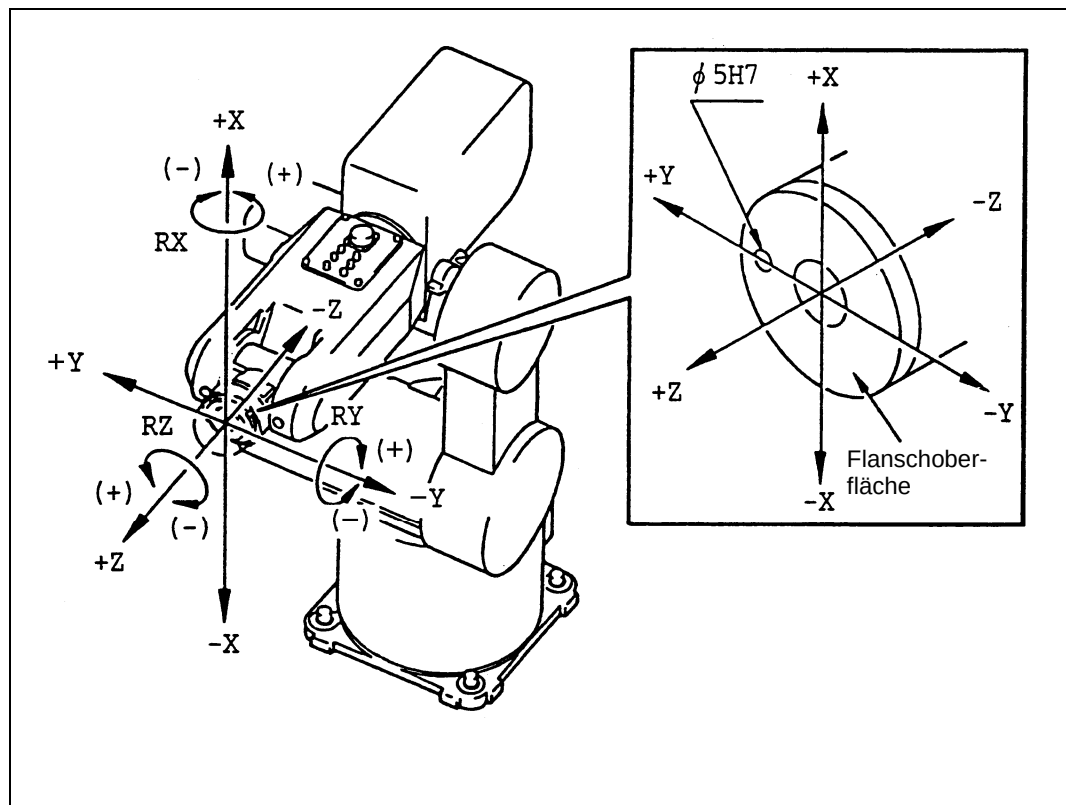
(a) Bewegungen im Werkzeugmodus
